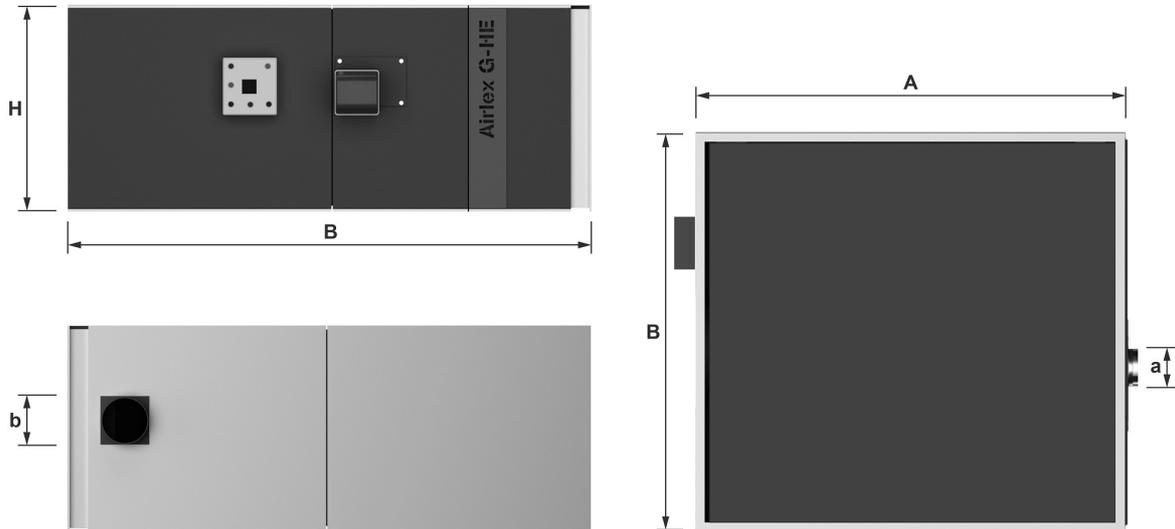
Воздухонагревателей Airlex V-HE
